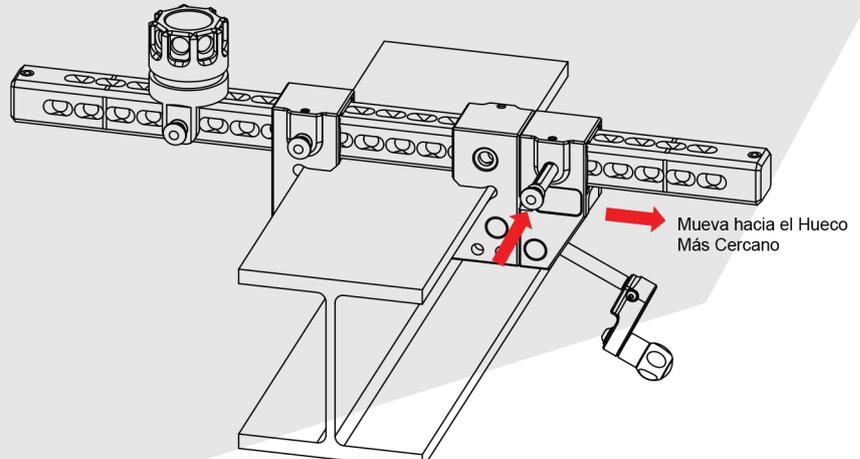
Instalación de Abrazadera de Viga I Paso 2
